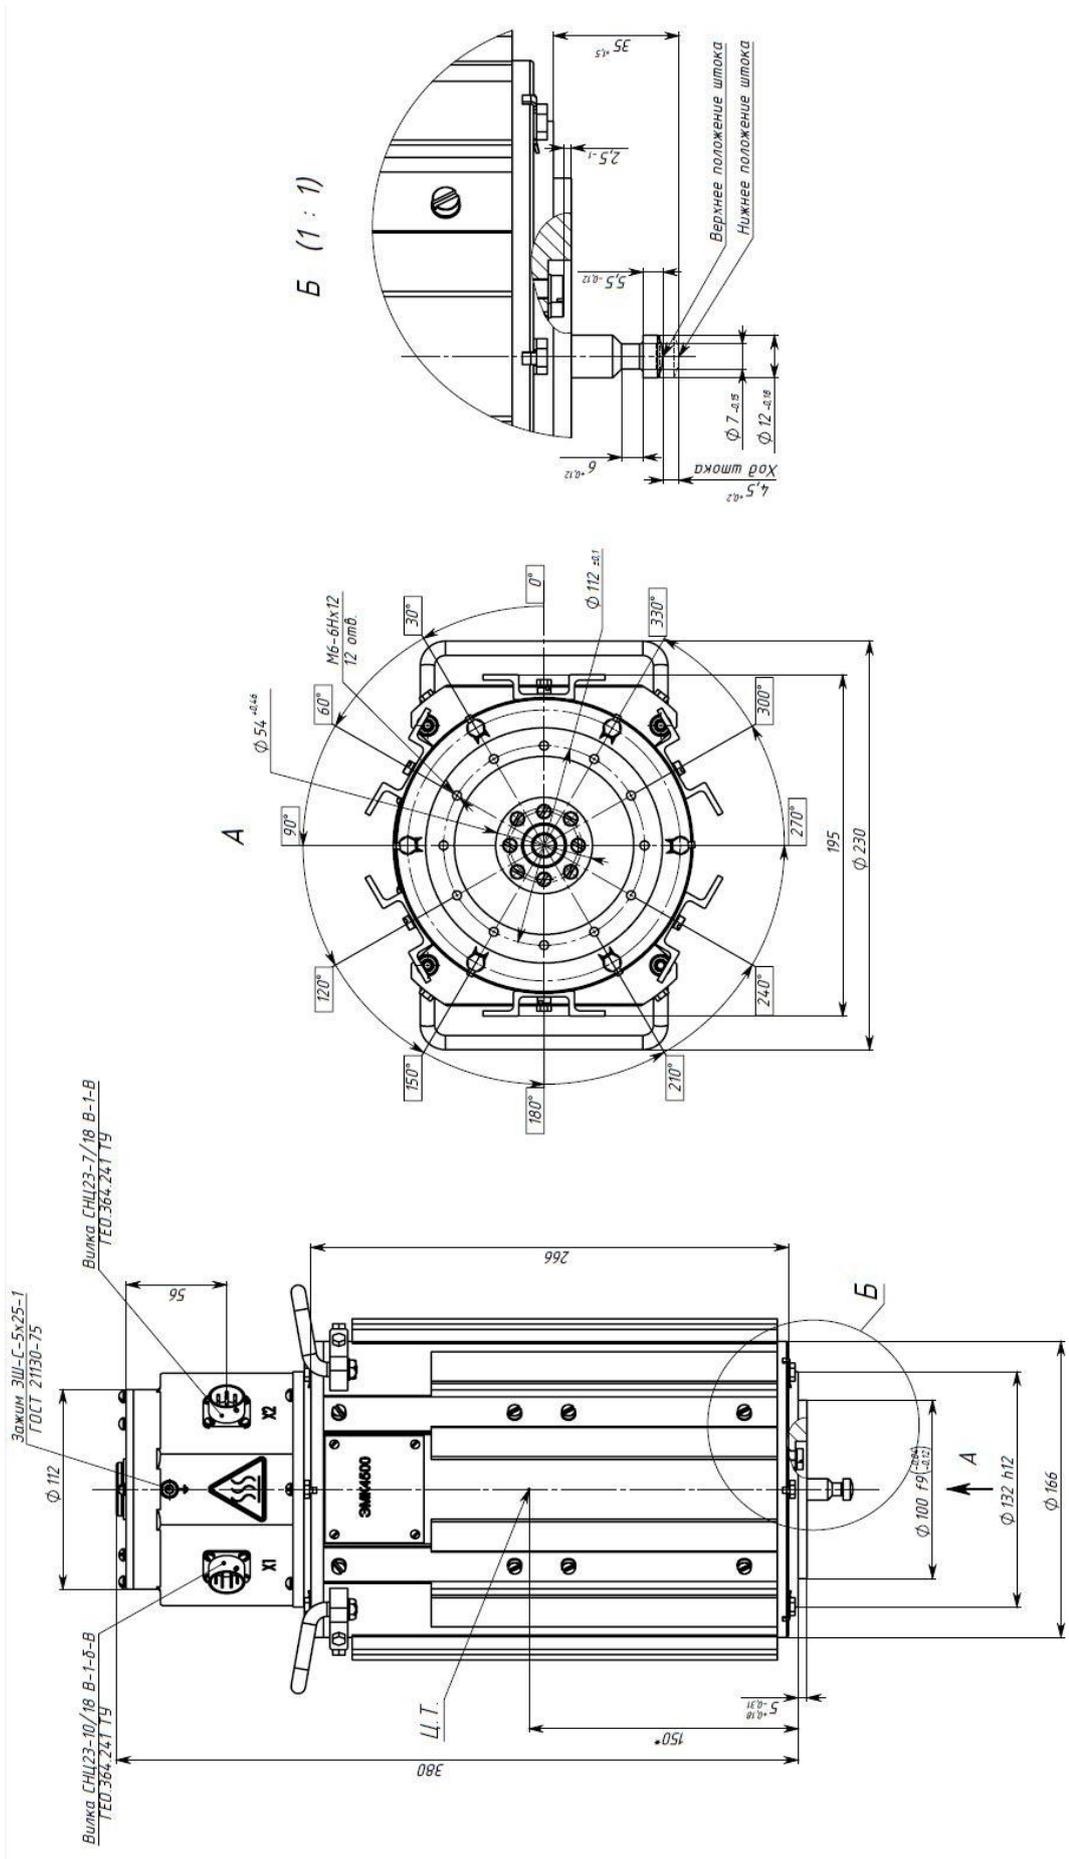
Габаритный чертеж привода ЭМК4500
